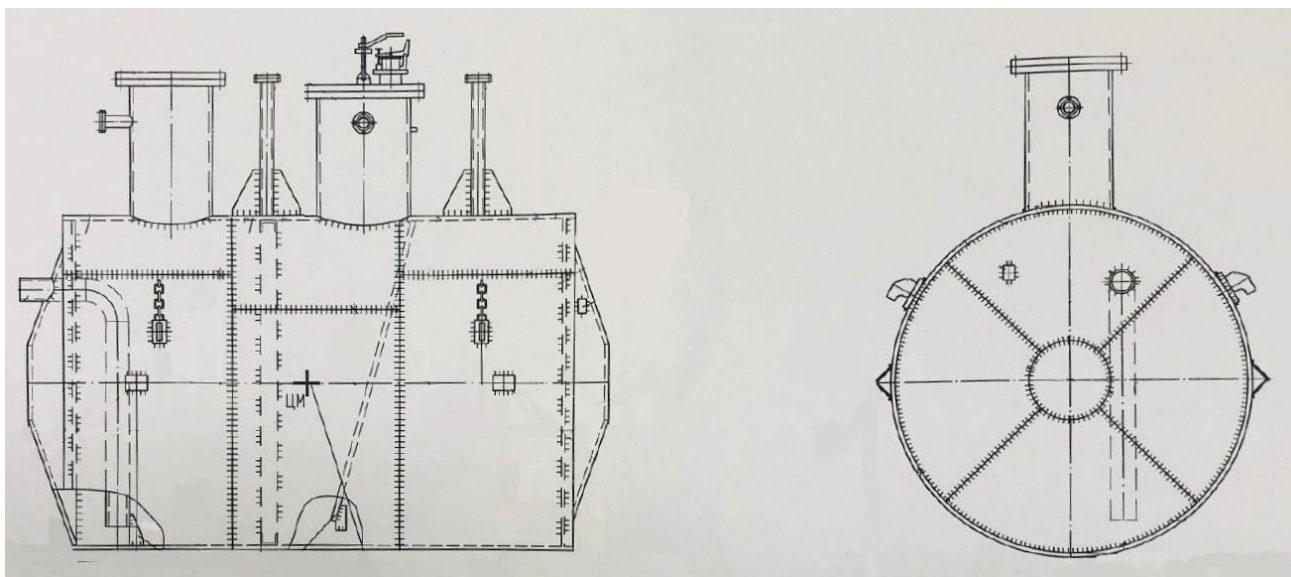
Общий вид эскиза резервуаров РГС-20
